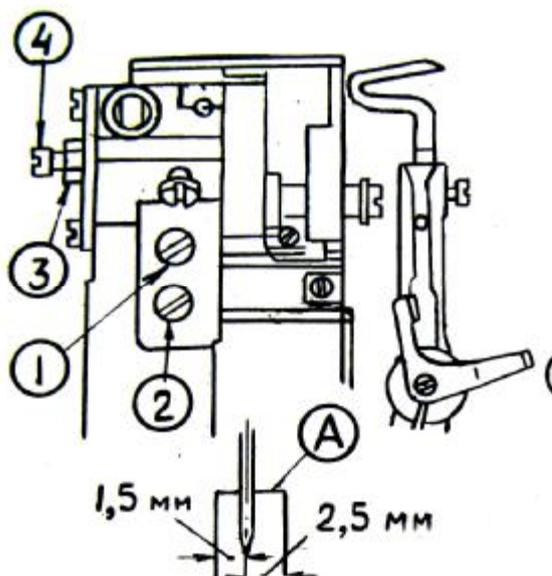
Регулировка положения предохранителя А и усилия нижнего ножа
